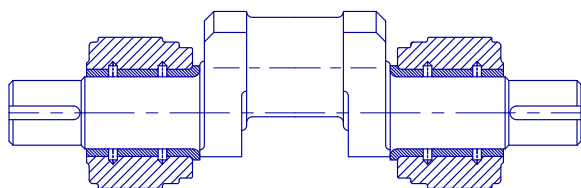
Ведущий вал главного исполнительного механизма кривошипно-шатунного пресса [17, 18]
